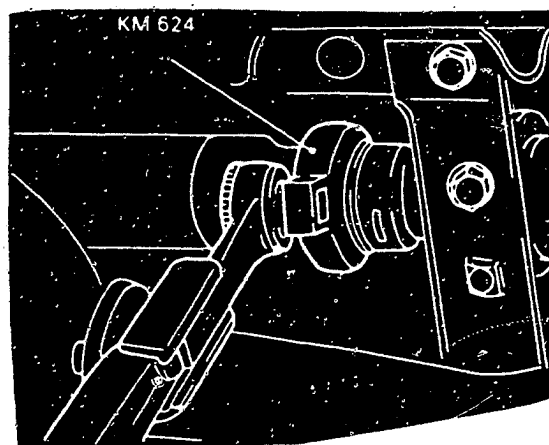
Lösen der Befestigungsmutter des Gelenkwellen-Schiebestückes mit Spezialwerkzeug.
